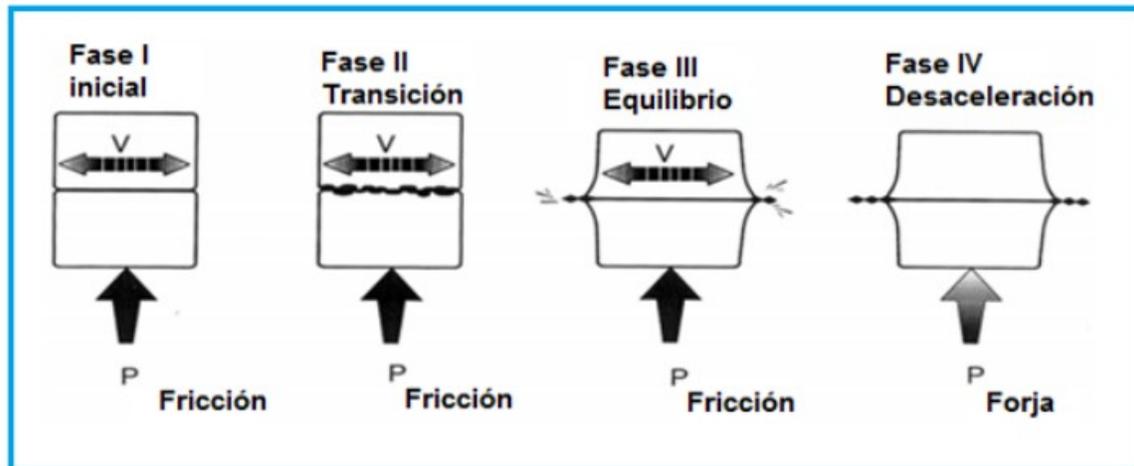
Fases del proceso de soldadura por fricción lineal.
